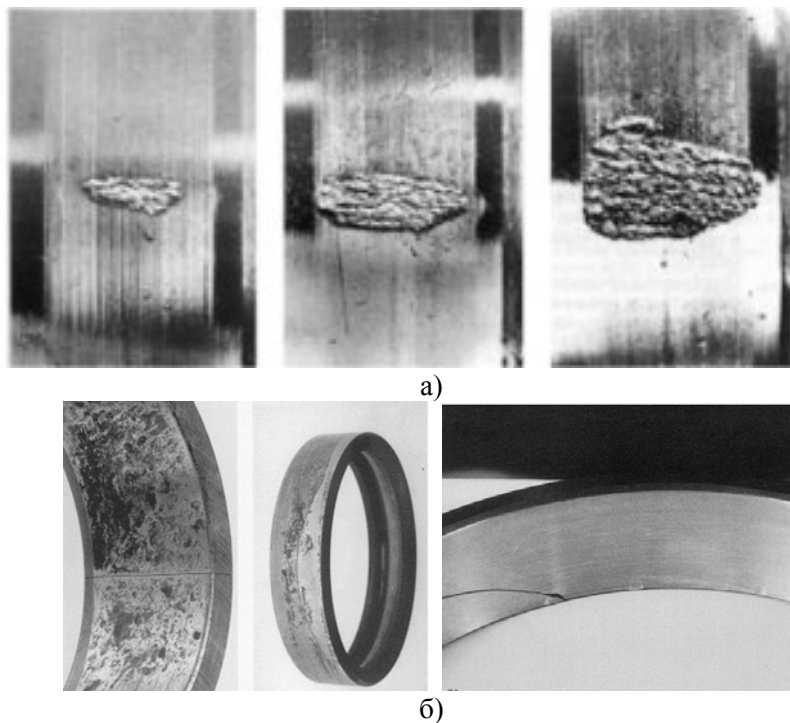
Виды повреждения колец подшипников качения. а)-поверхностные стадии развития усталостной раковины; б)- трещины в кольцах, обусловленные прорастанием поверхностных или внутренних повреждений, контактной коррозией и неправильной сборкой
